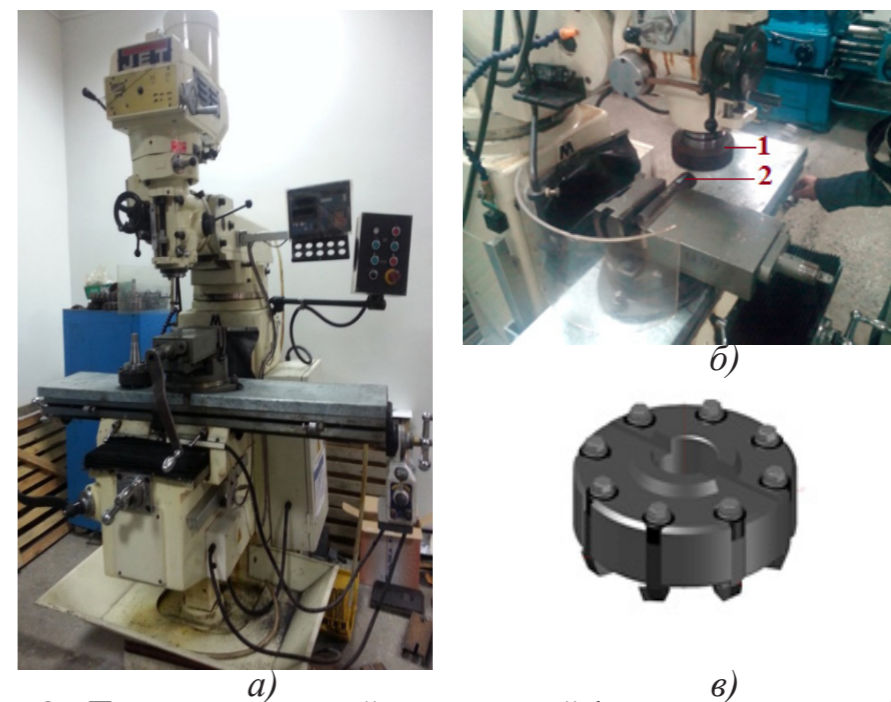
Полуавтоматический вертикальный фрезерно-сверлильный станок, режущий инструмент и процесс обработки
